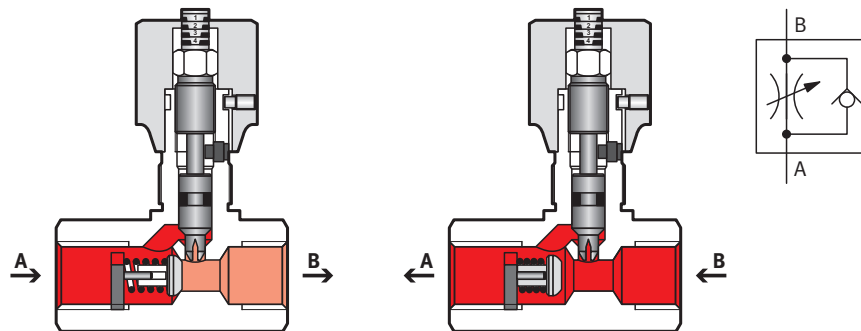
válvula de estrangulación y antirretorno. Vistas en corte y símbolo.
